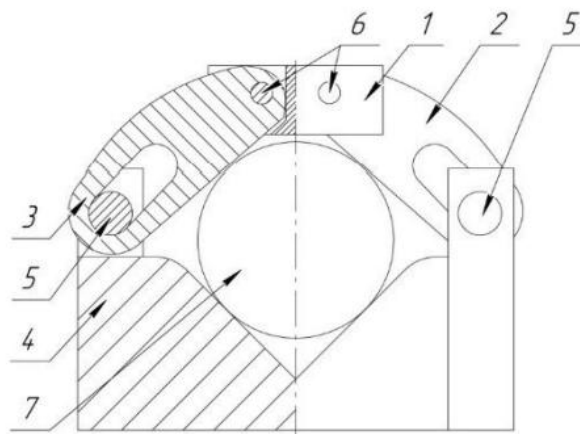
Устройство для кузнечной протяжки с подвижными рабочими элементами: 1 – верхний боек; 2, 3 – подвижные рабочие элементы; 4 – нижний боек; 5 – шарниры нижнего бойка; 6 – шарниры верхнего бойка; 7 – заготовка [4]
